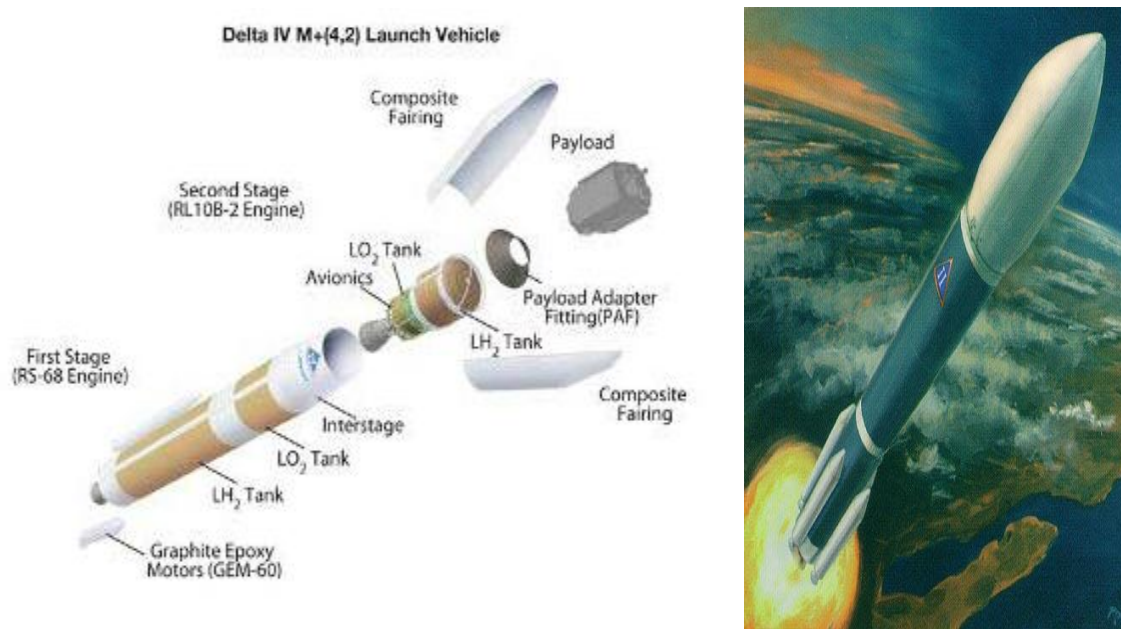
Boeing Delta II, Delta IV Expendable Launch Vehicles (vehículo de lanzamiento desechable) donde el tanque esta soldado por la técnica de FSW
